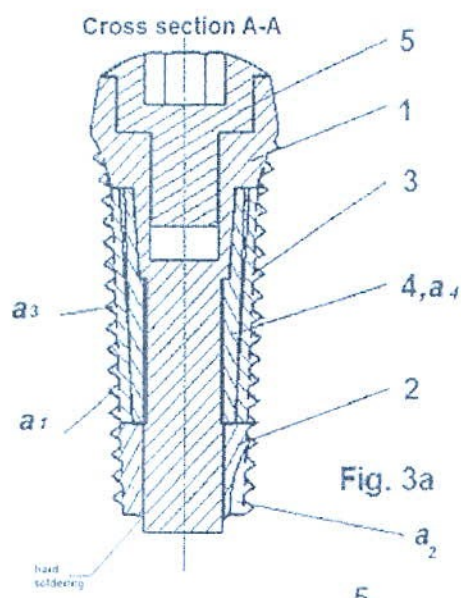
de la presente invención, sección longitudinal sobre el plano AA del implante.
